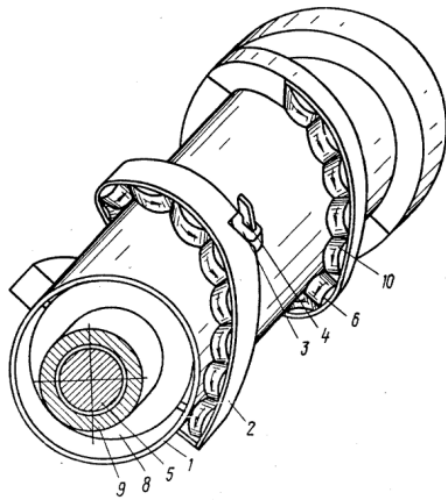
Шнековый исполнительный орган с дополнительными погрузочными устройствами:
